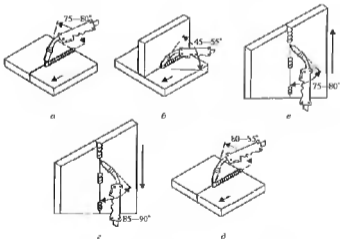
Угол наклона сварочной горелки при выполнении различных швов в нижнем и вертикальном положениях при циклическом режиме сварки короткой дугой (а — г) и при струйном переносе металла (д)
